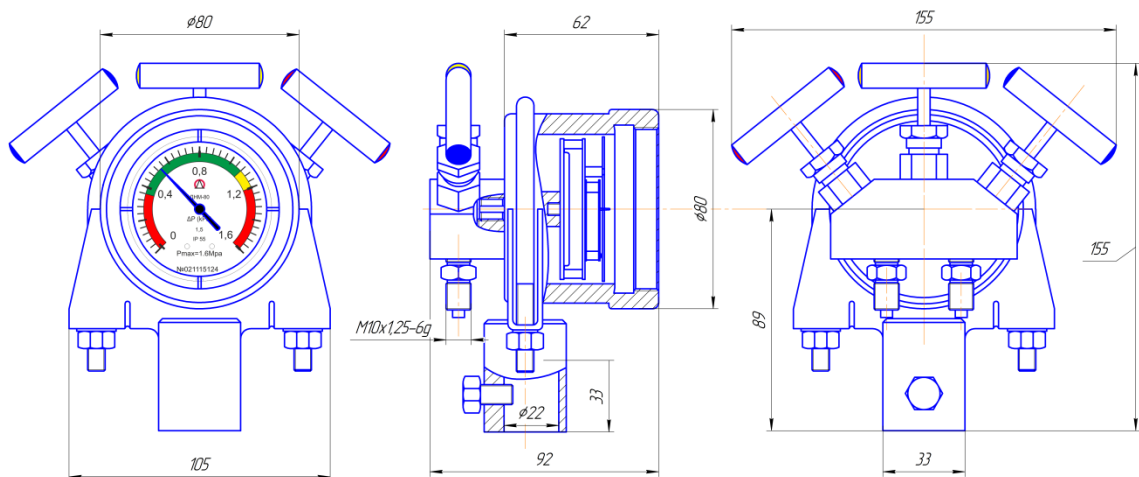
Габаритные и присоединительные размеры ДНМ-80
